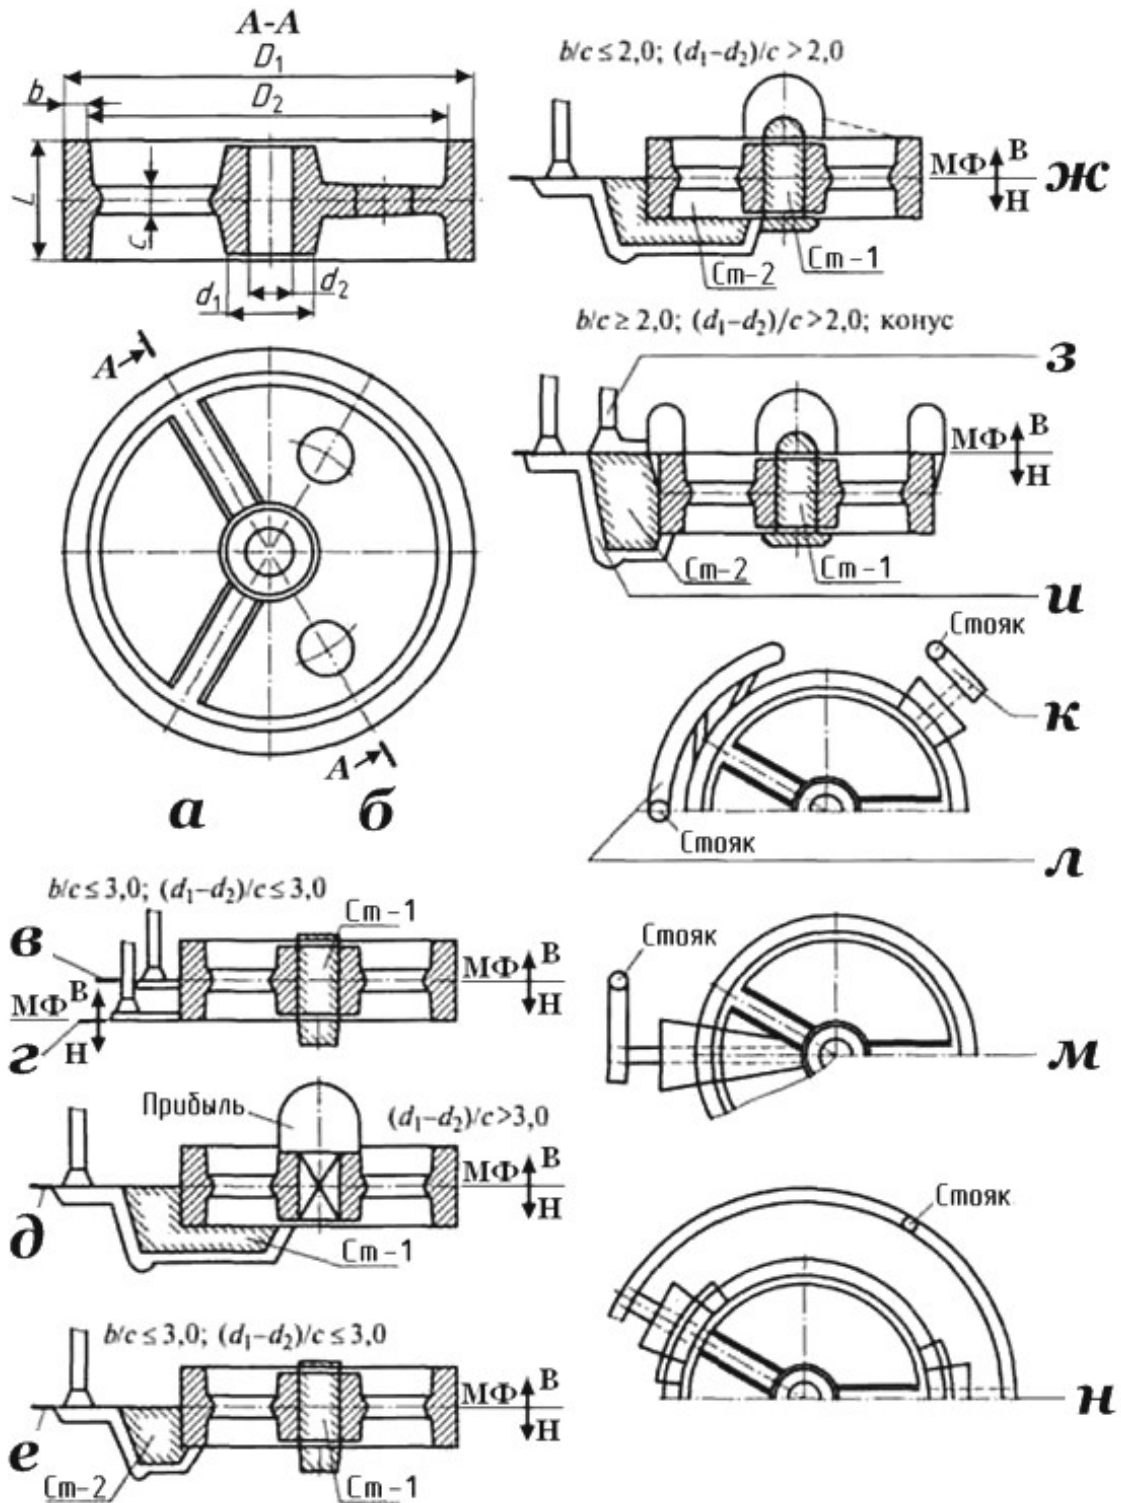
Конструкции деталей отливок типа «колесо» при соединении обода и ступицы: а – спицами; б – диском с отверстиями; в–н – варианты технологических процессов изготовления отливок; D_1 – наружный диаметр колеса; d_1 – наружный диаметр ступицы; d_2 – диаметр отверстия в ступице; L – толщина колеса; b – толщина обода; c – толщина спицы (или диска); D_2 – внутренний диаметр обода
